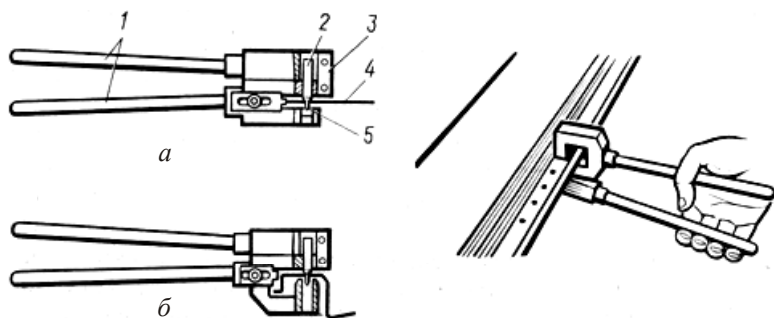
Ручные дыроколы для пробивки отверстий:
